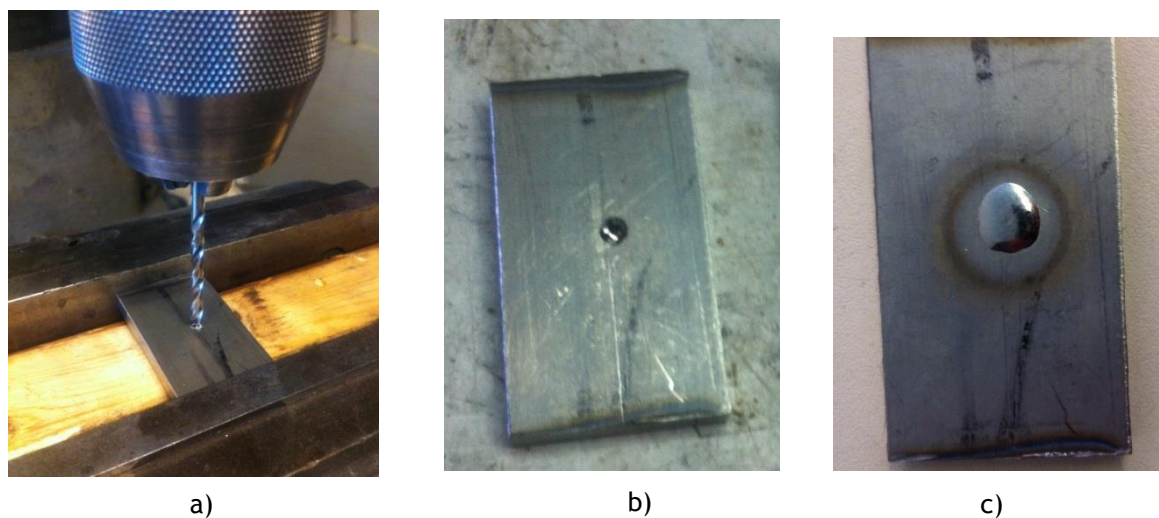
Furação das barras de Ti-6Al-4V: a) processo de furação b) furo final c) furo reparado por soldadura TIG
